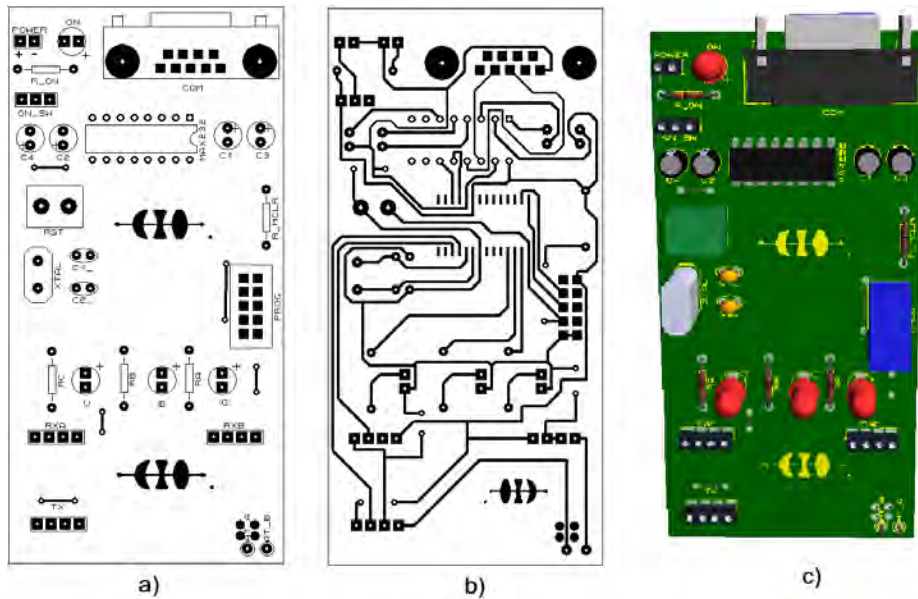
Diseño del subsistema de comunicación. a) Diseño de la parte superior de la placa. b) Diseño de la parte inferior de la placa. c) Simulación 3D de la placa.
